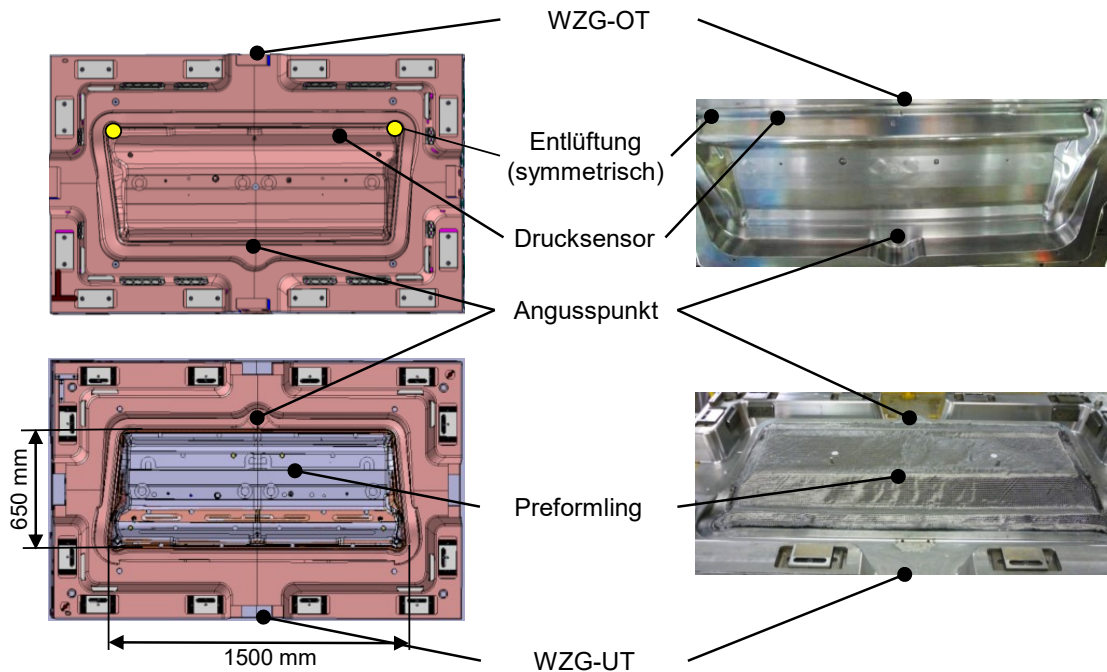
Werkzeugober- und -unterteil des Bodenwerkzeugs.
